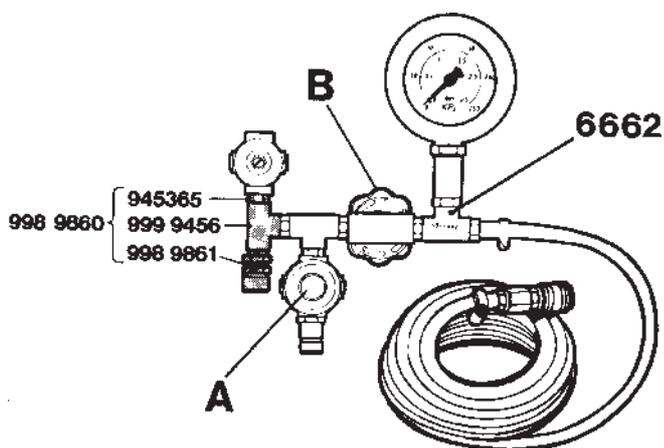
Montage du kit 998 9860 pour dispositif d'essai sous pression 6662 (Suède seulement)
